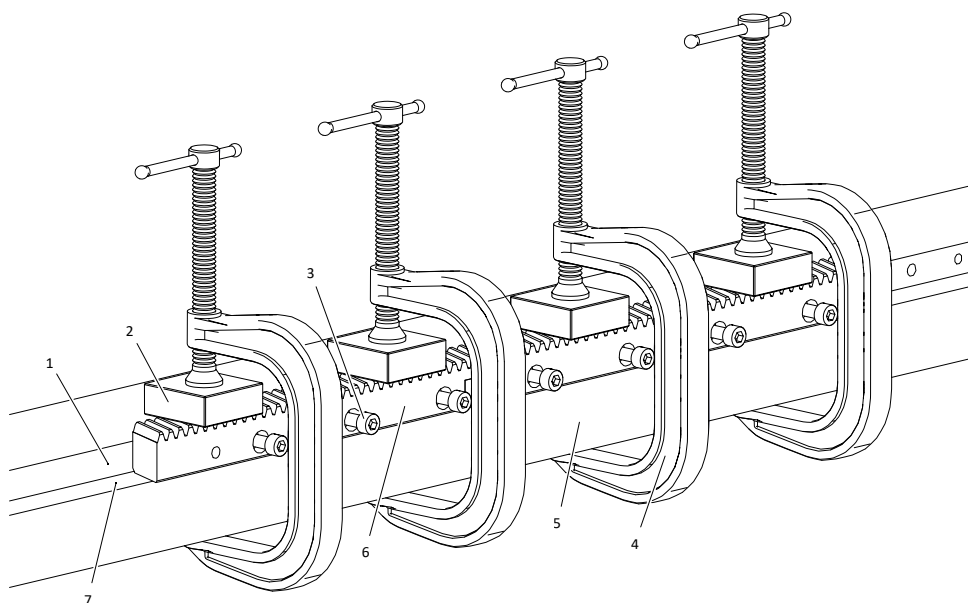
Montaje de una cremallera en la estructura de conexión (ejemplo)
